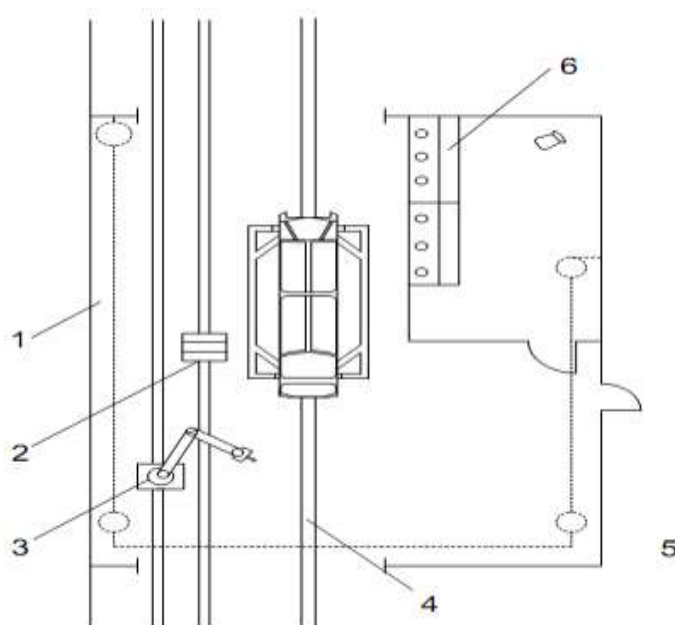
Схема поста сварки лонжерона на кузов
